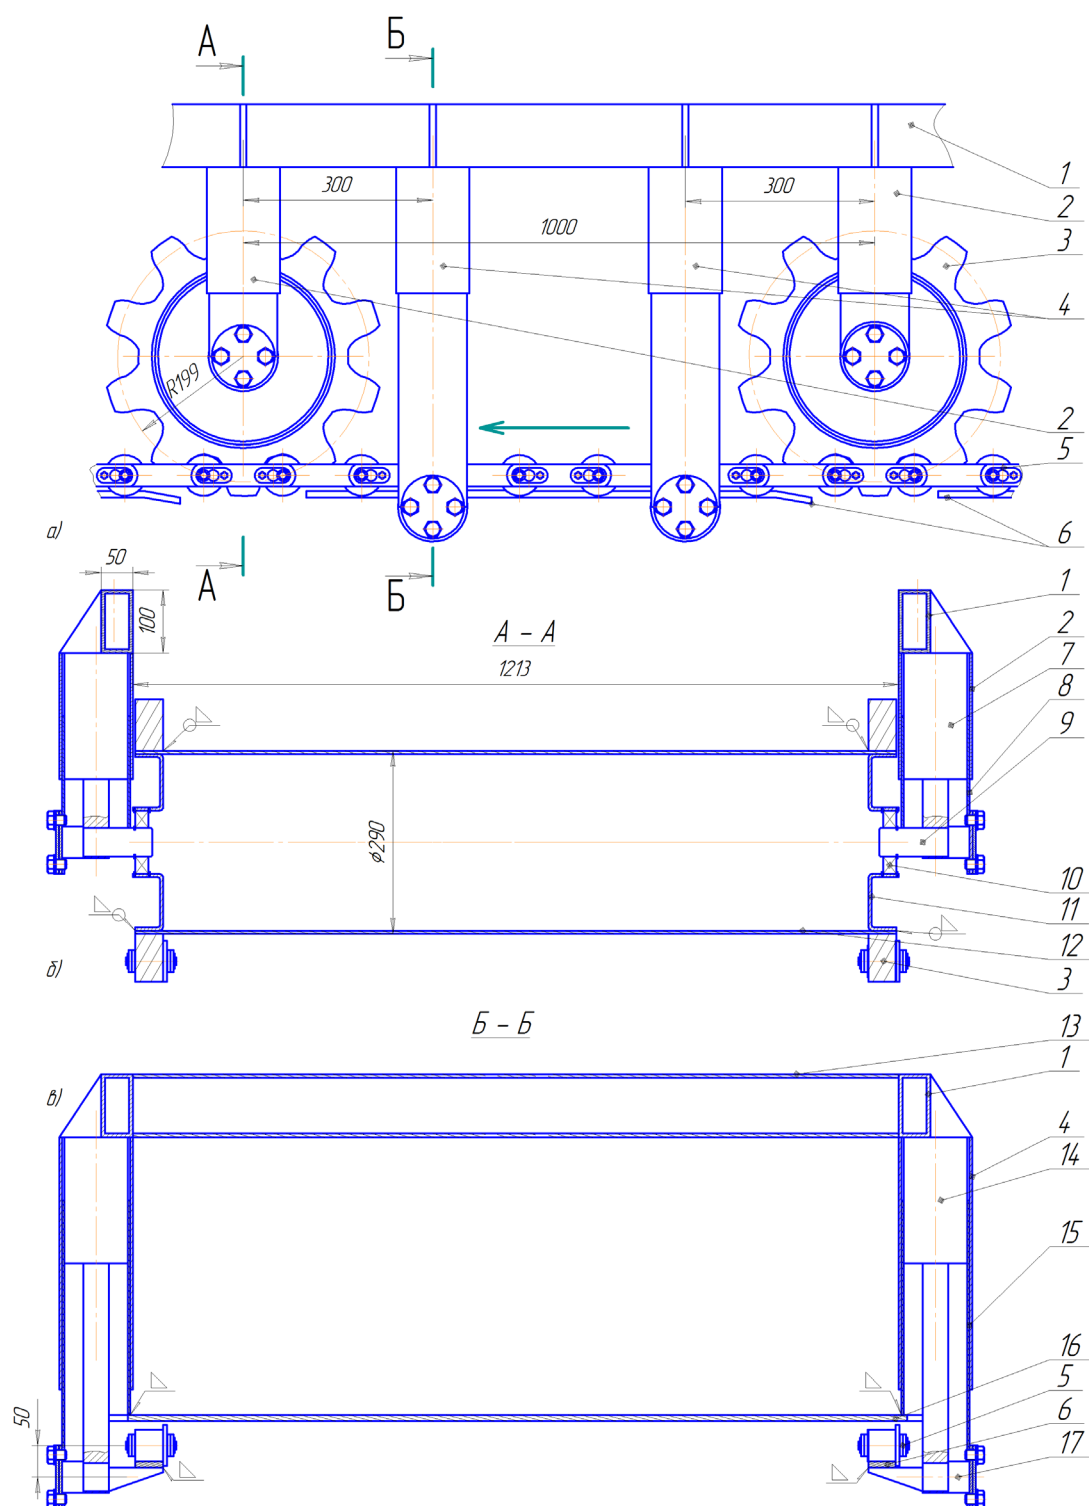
Подвеска цепей: а – вид сбоку (сзади по ходу агрегата); б – сечение А – А; в – сечение Б – Б; 1 – лонжерон (средней или правой рамы); 2, 4 – внешняя направляющая; 3 – ролик; 5 – цепь; 6 – поддерживающая планка; 7 – гидроцилиндр роликов; 8, 15 – внутренняя направляющая; 9, 17 – цапфа; 10 – подшипник; 11 – диск; 12 – трубчатая ось; 13 – траверса; 14 – гидроцилиндр поддержки; 16 – связь
